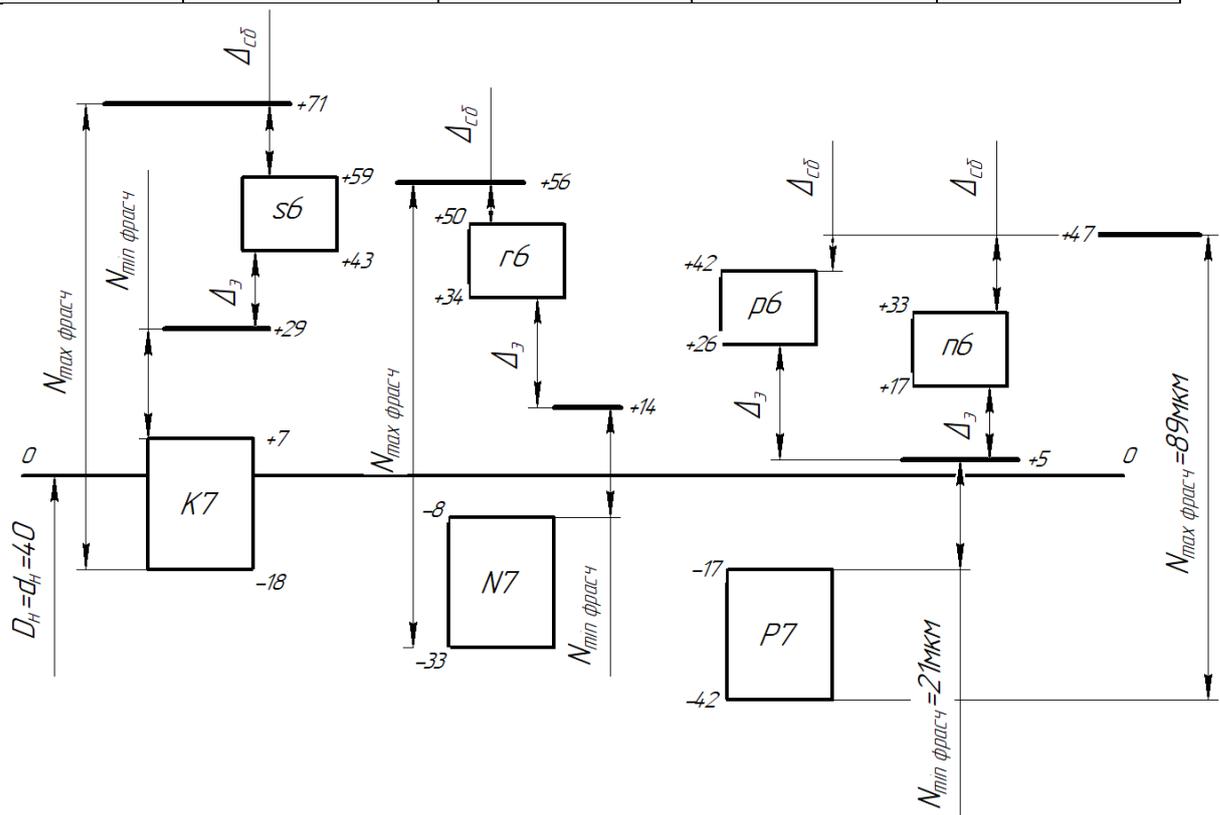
Схема полей допусков комбинированных посадок
